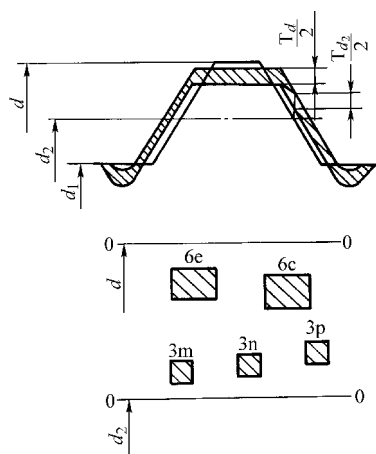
过盈配合螺纹外螺纹公差带
